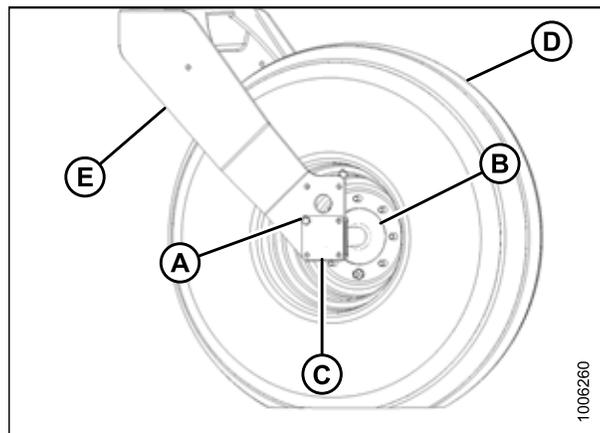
Самоустанавливающееся колесо в сборе и балансир (вид в положении двигателем вперед)
